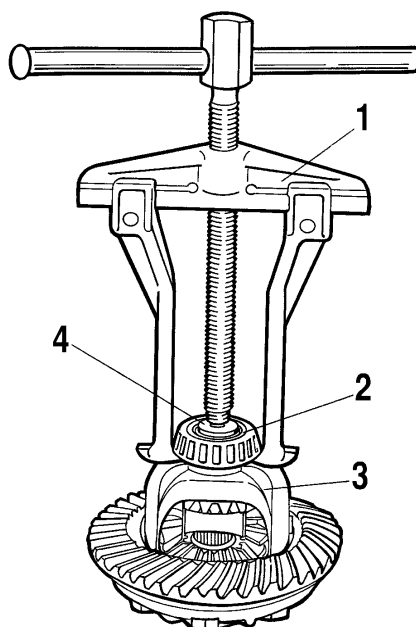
Снятие внутреннего кольца заднего подшипника ведущей шестерни универсальным съемником:
